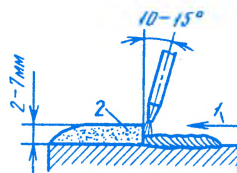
Положение угольного электрода в процессе наплавки порошковых сплавов:
